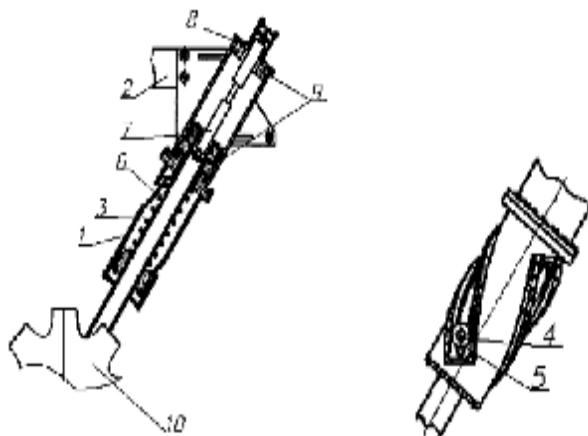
Предохранительное устройство почвообрабатывающего орудия
